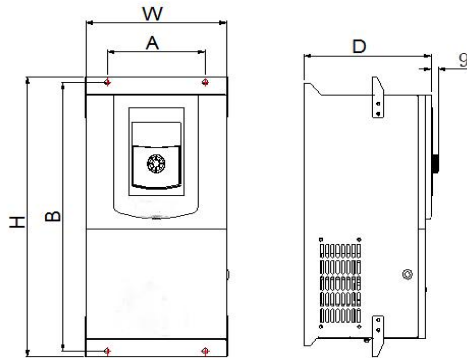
380V (4T) 18.5~37kW 钣金机箱外形尺寸及安装尺寸示意图
